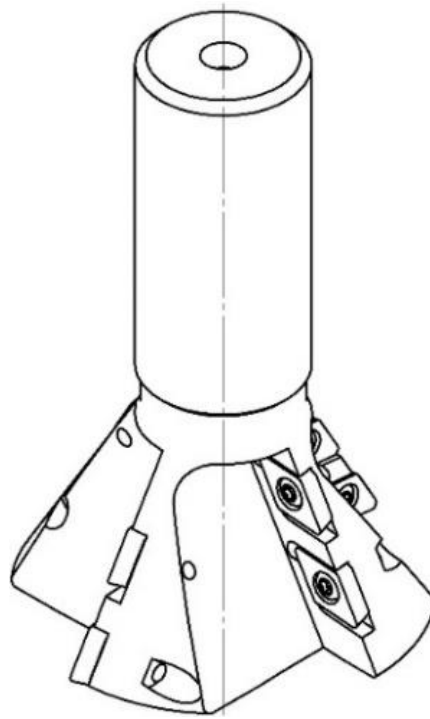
Кінцева синтезована фреза для оброблення елементів з'єднання типу "хвіст ластівки" зі змінними різальними елементами – пластинами
